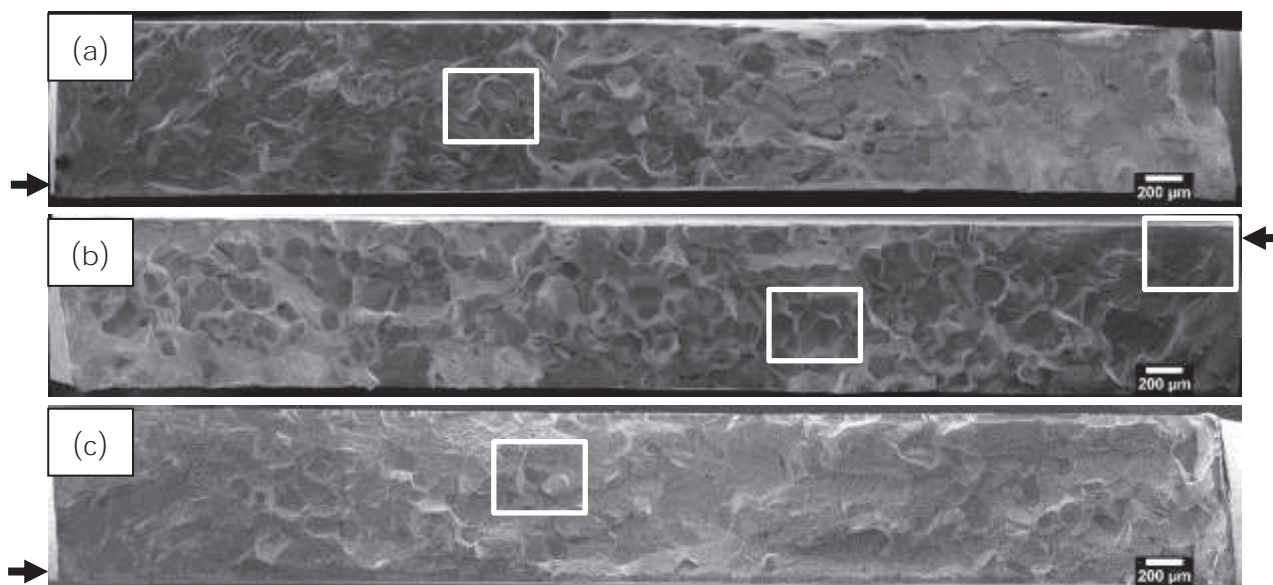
Faciès de rupture des éprouvettes rompues en fatigue à température ambiante, éprouvette non vieillie (a) et éprouvettes vieilles pendant 500h à 450°C (b) et 600°C (c)
